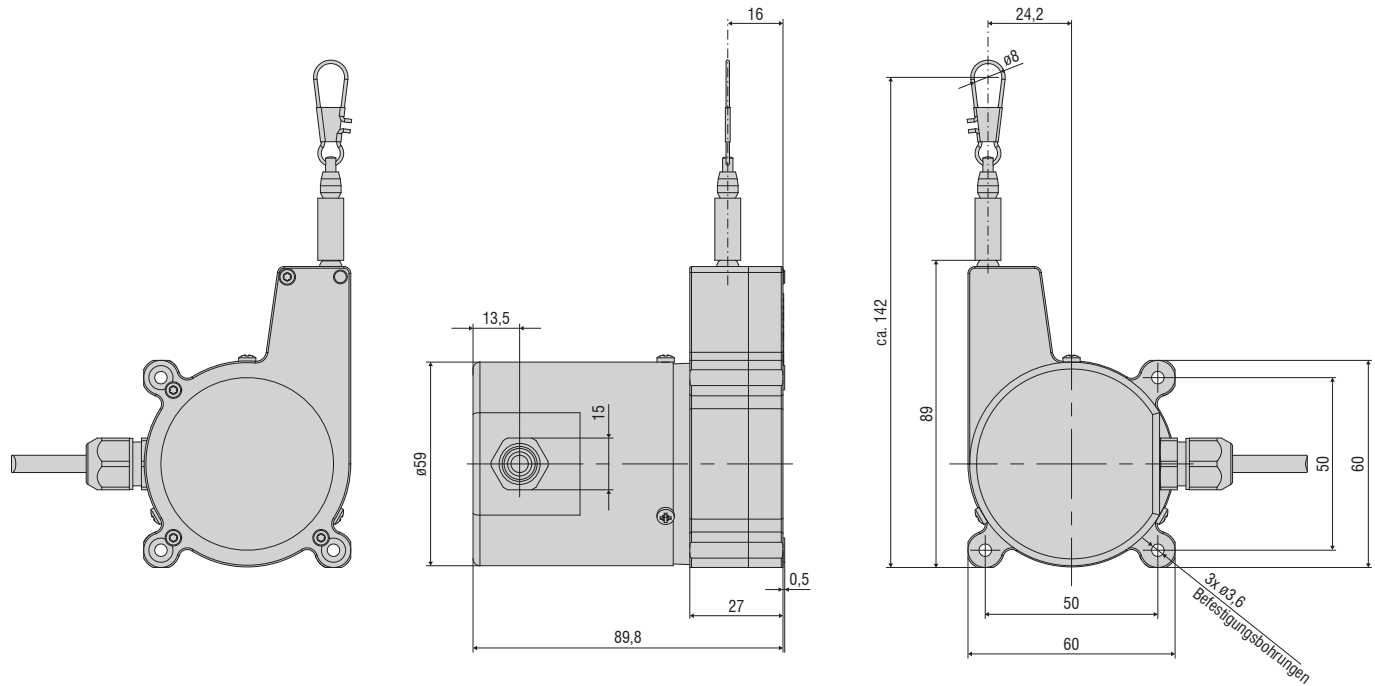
Maßzeichnung WPS-xxx-MK60-CR-TTLxx mit TTL01, TTL02, Abmessungen in mm
